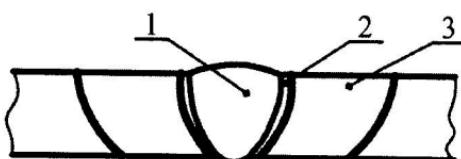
Схема будови зварного з'єднання: 1 – зварний шов; 2 – зона сплавлення, 3 – зона термічного впливу
